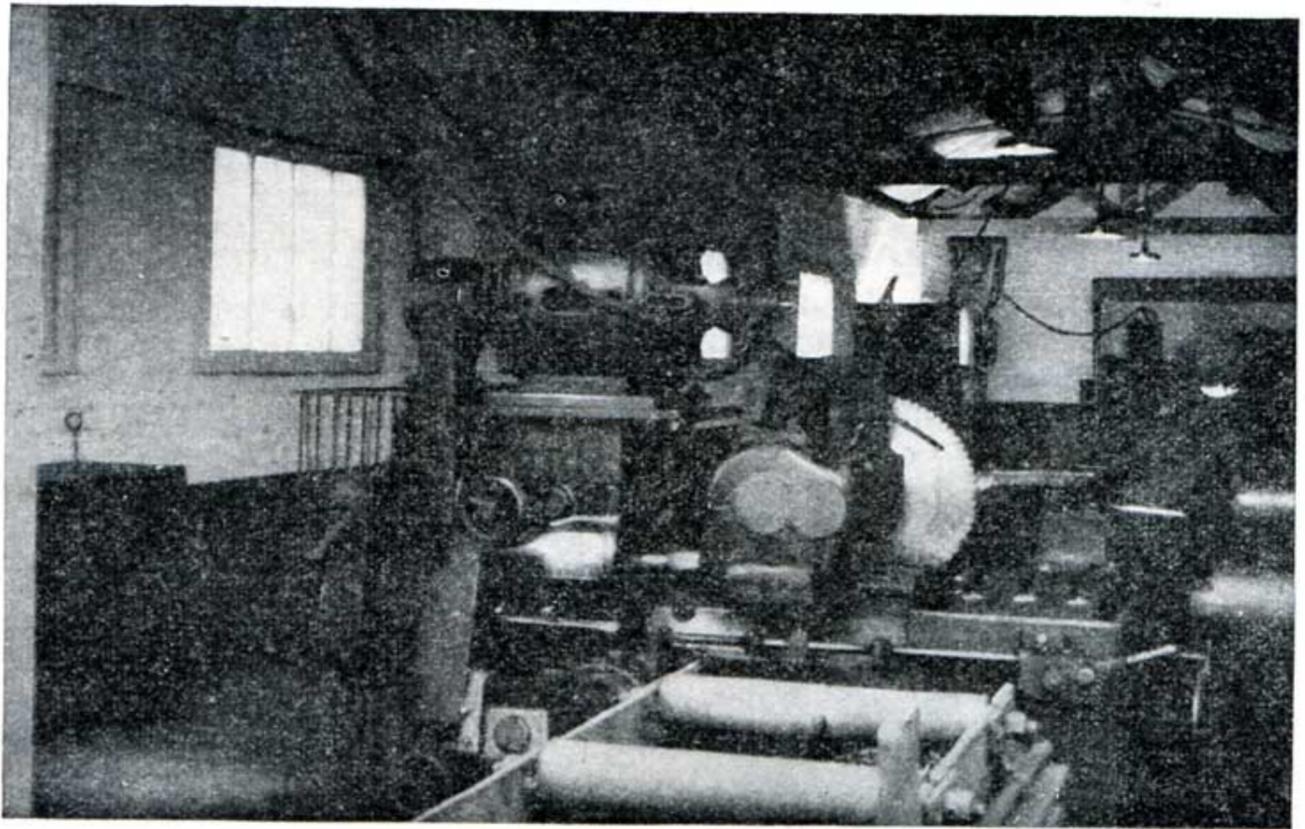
Machines combinées pour le sciage et le forage des rails aux deux bouts simultanément.
